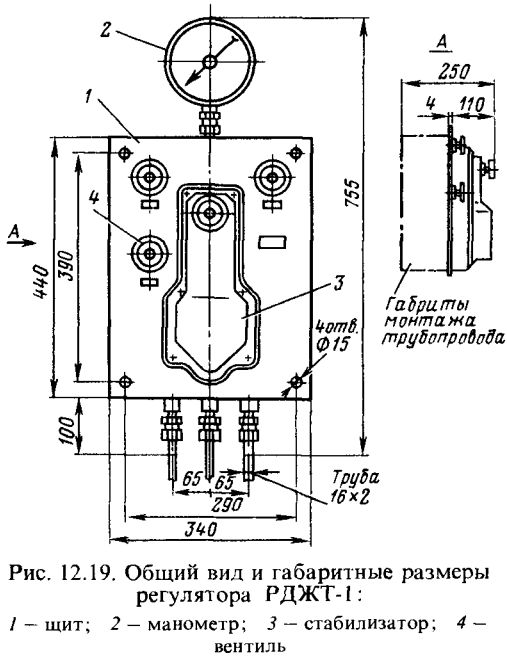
Общий вид и габаритные размеры регулятора РДЖТ-1:
